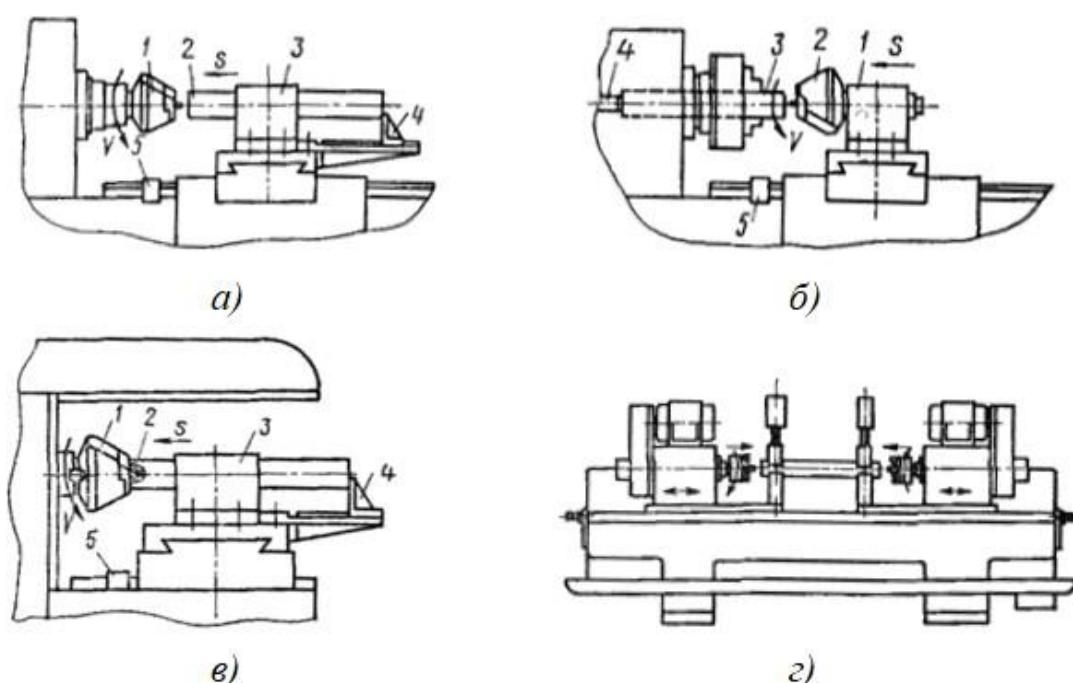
Схеми центрування за допомогою спеціальної інструментальної головки [3]
